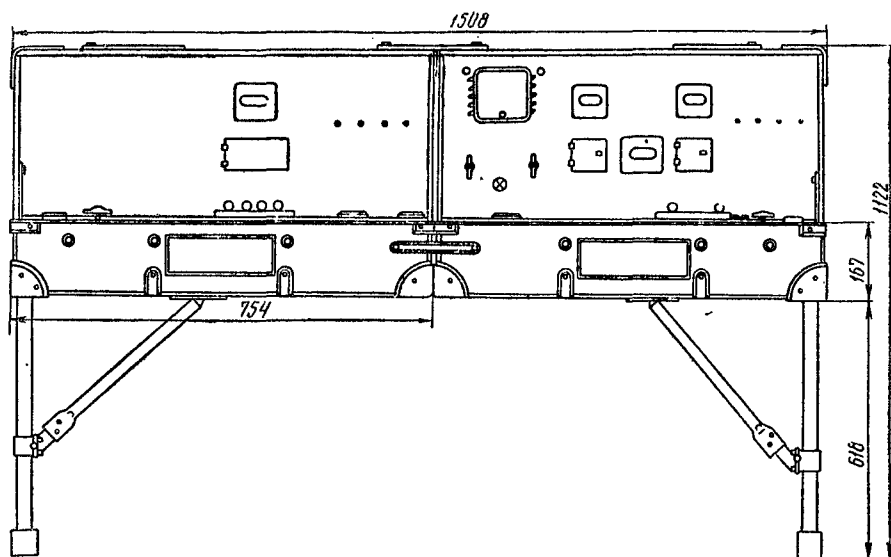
Общий вид конструкции сборно-разборного стенда для проверки реле
